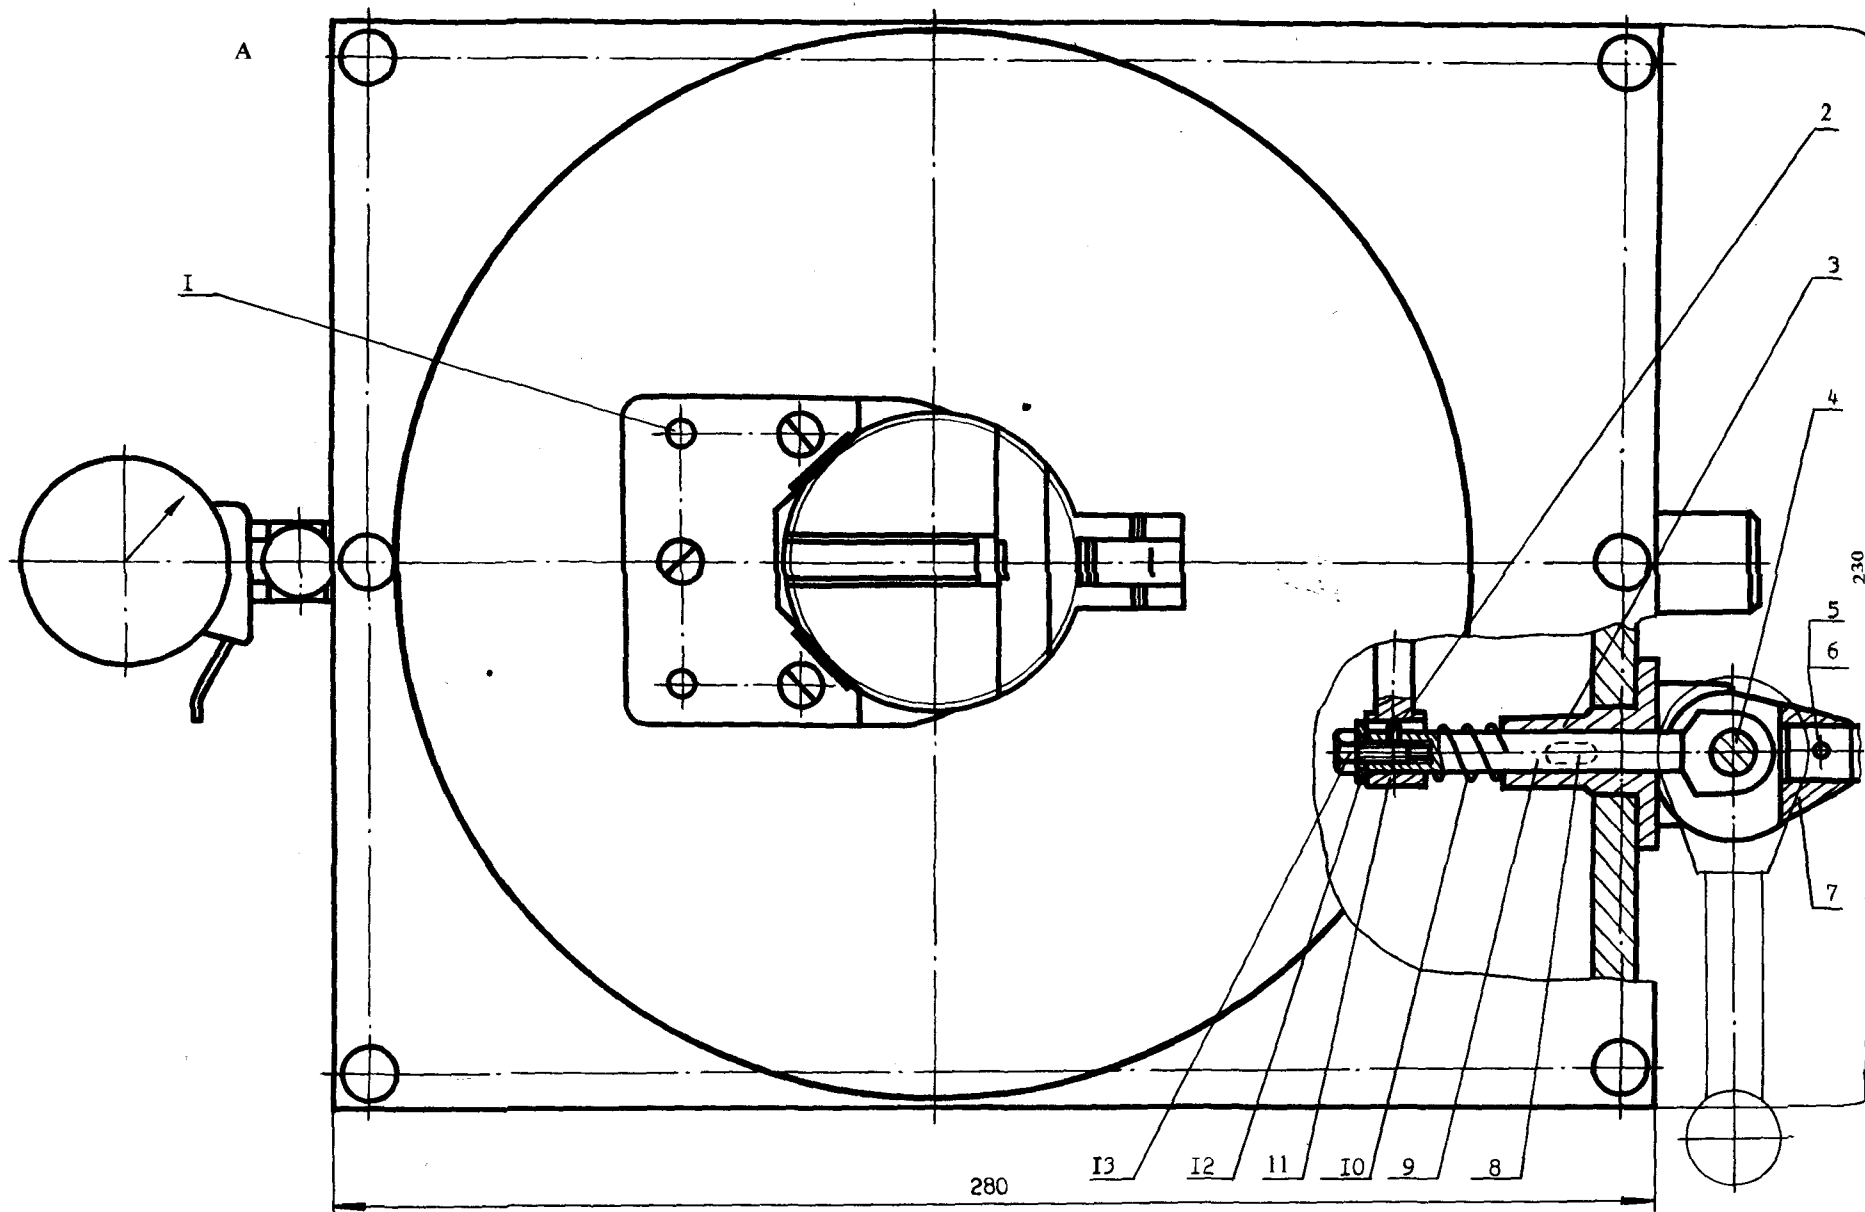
Контрольное приспособление для ступенчатого диска (вид А на рис. 2.11):
